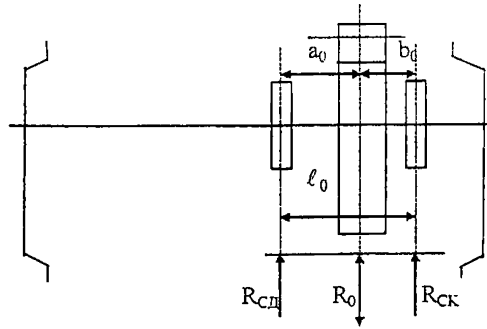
Схема для определения нагрузок на опорные подшипники тягового редуктора
